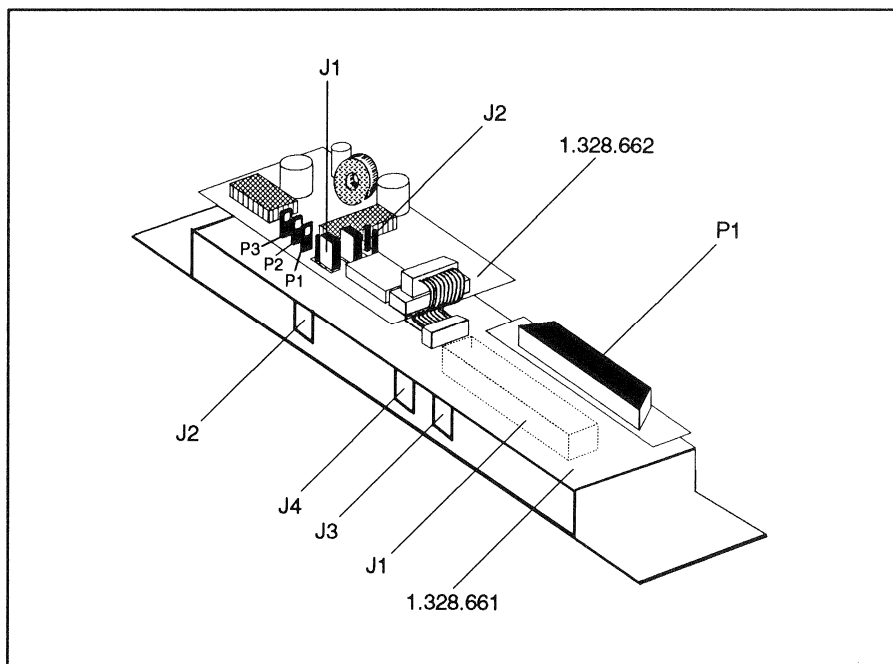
Jumper und Anschlüsse der parallelen Fernbedienung.
